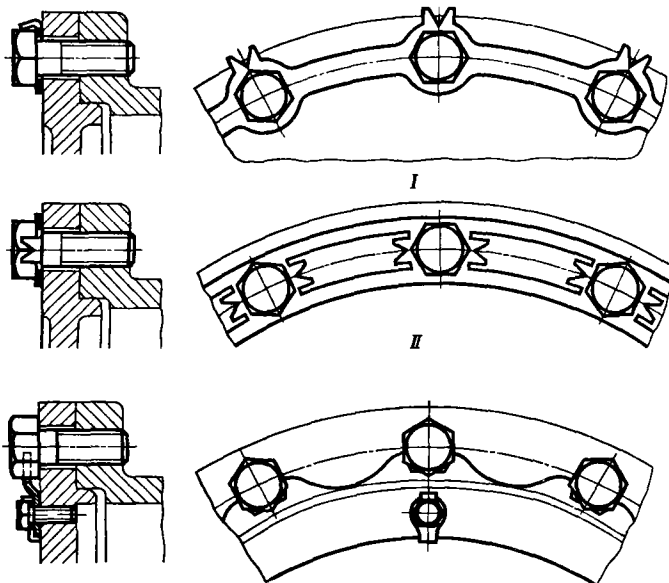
Стопорение болтов на цилиндрическом фланце подкладным кольцом с отгибными лапками
